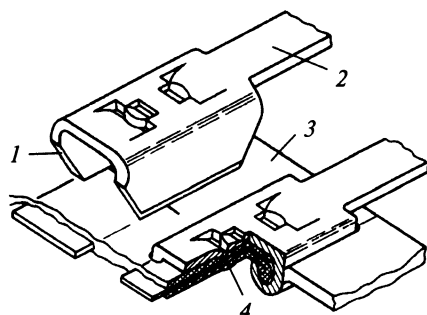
Монтаж методом прокалывания изоляции проводов:
